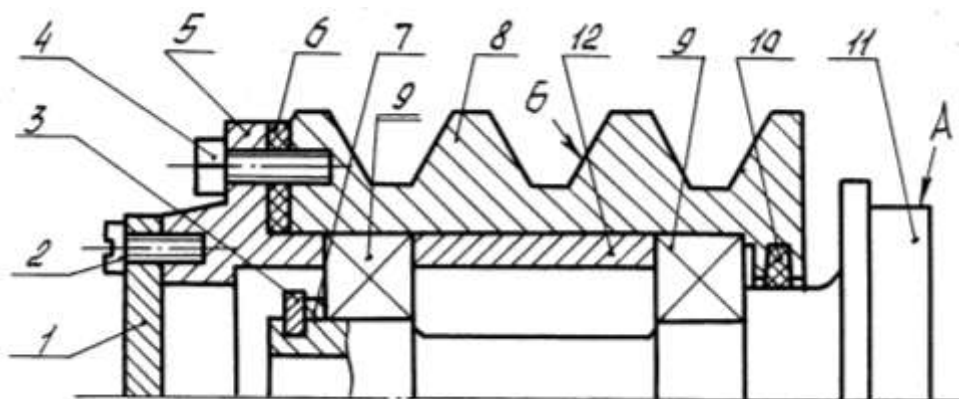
Эскиз сборочной единицы (Сб.11 – Ступица)
